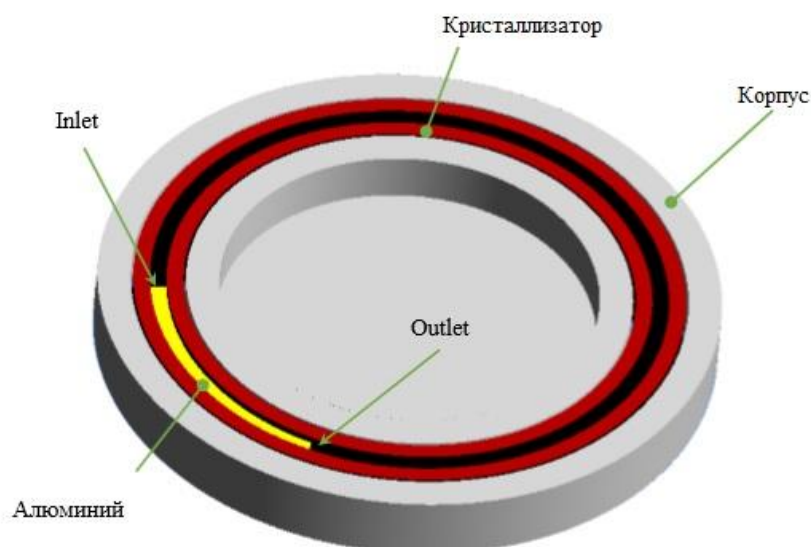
Компьютерная модель установки непрерывного литья и прессования цветных металлов
